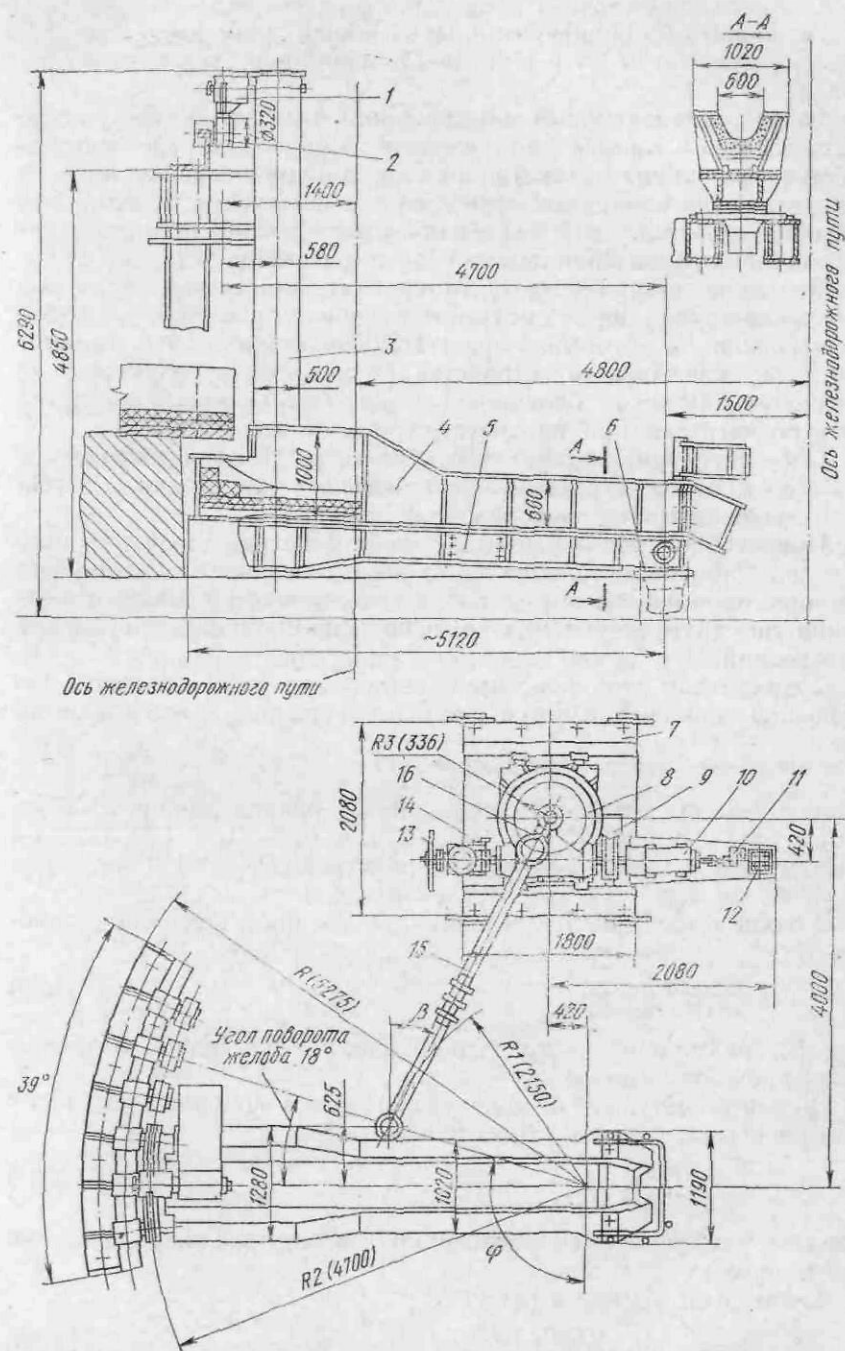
Поворотный желоб с верхним расположением роликовой дорожки
